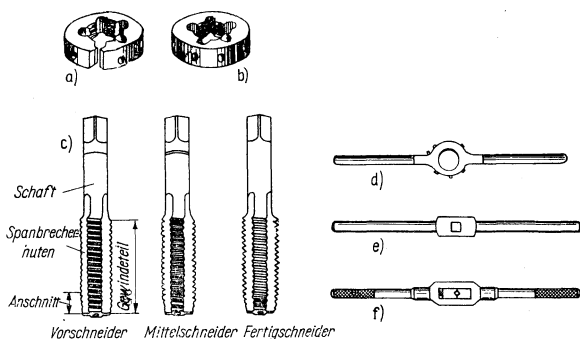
Gewindeschneidwerkzeuge; offenes Schneideisen (a), geschlossenes Schneideisen (b), ein kompletter Satz Gewindebohrer (c), Schneideisenhalter (d), Einlochwindeisen (e) und verstellbares Windeisen (f) für Gewindebohrer
